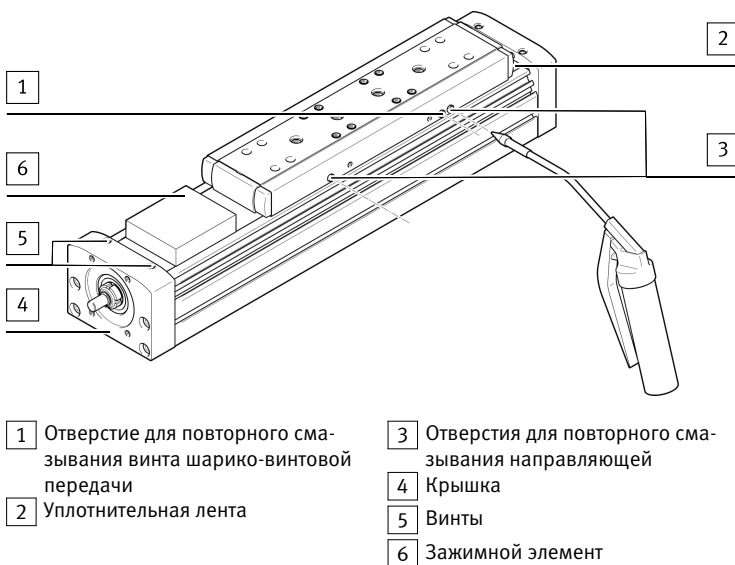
Смазывание винта шарико-винтовой передачи и направляющей
